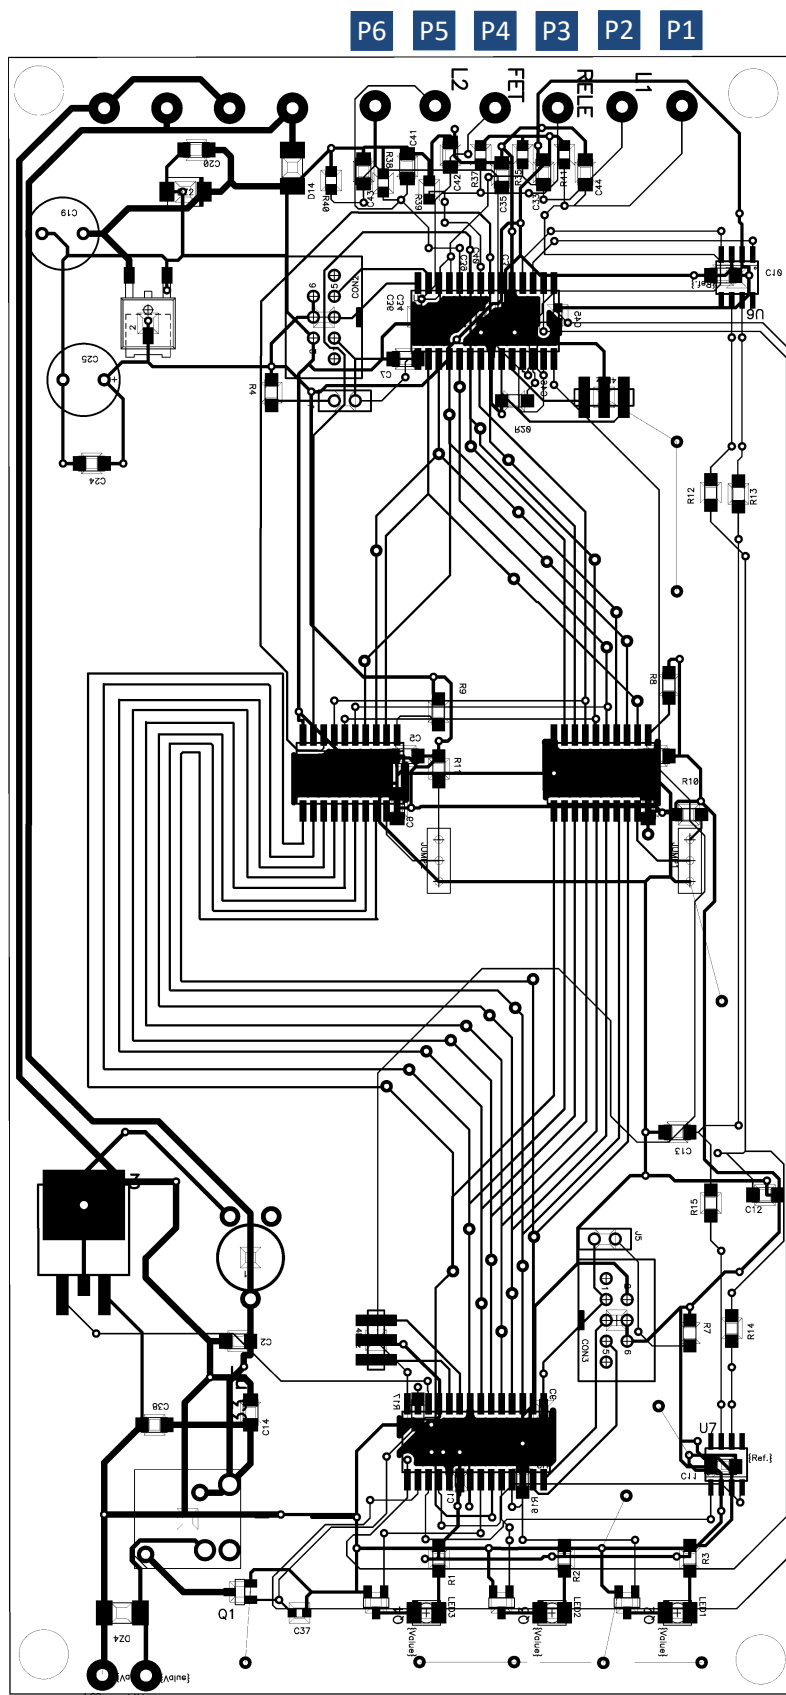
PCB, placement i routing de la placa que fem servir al laboratori.
